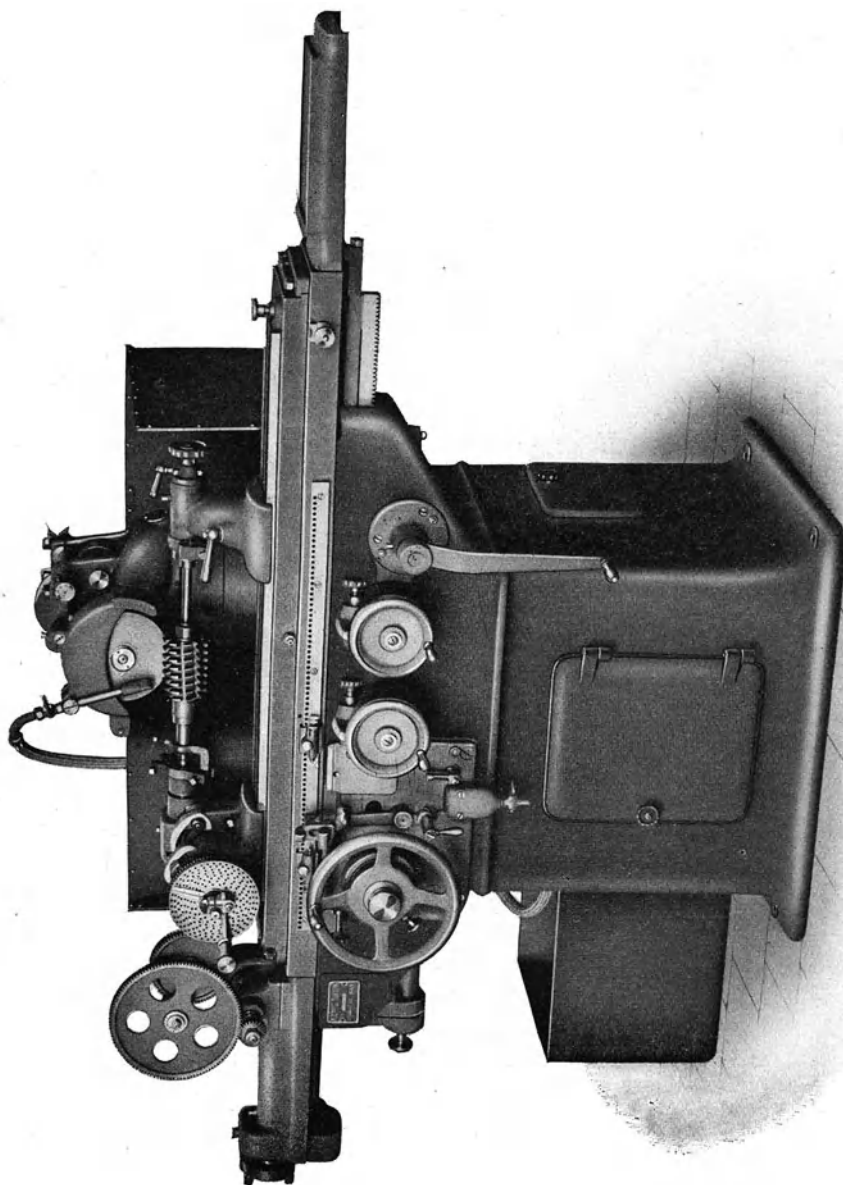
Die Universal-Werkzeug-Schleifmaschine der Naxos-Union.
